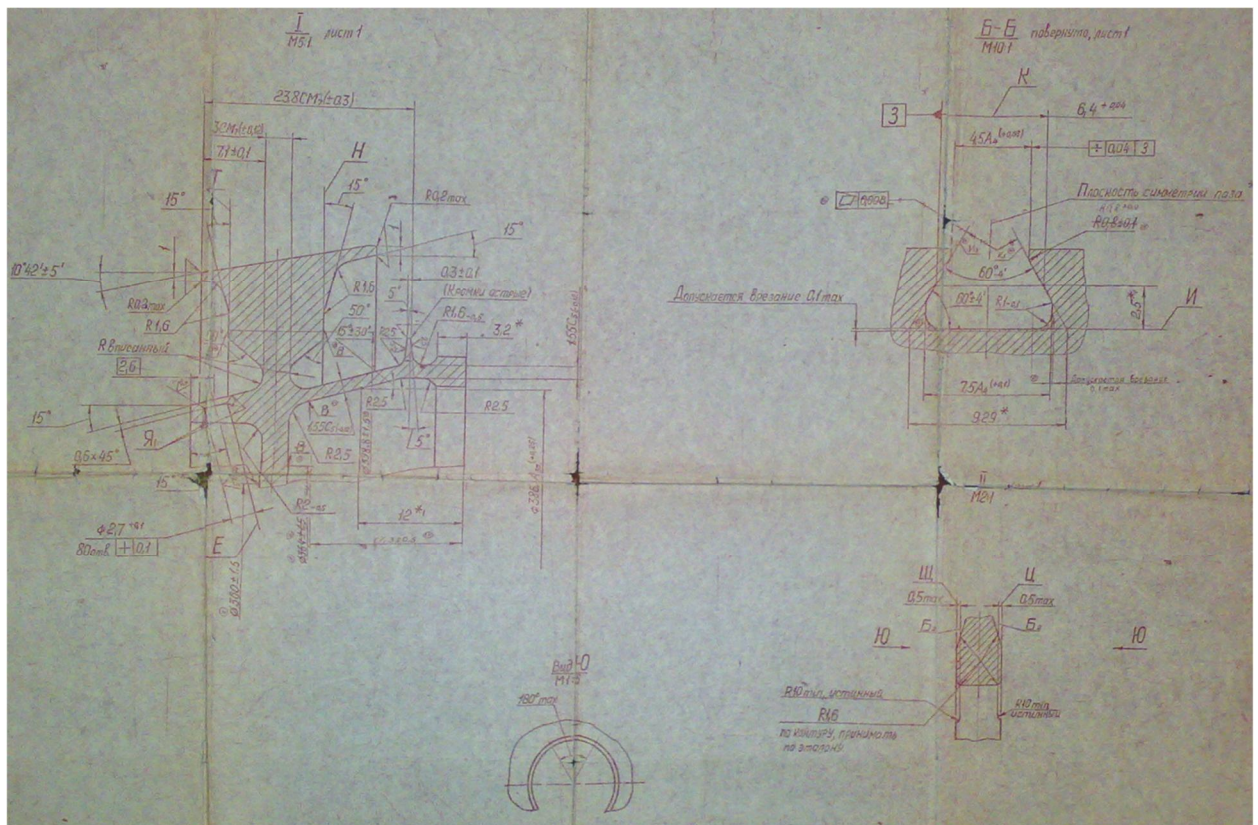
Фото креслення компресорного диска ТРД (Лист 2)
